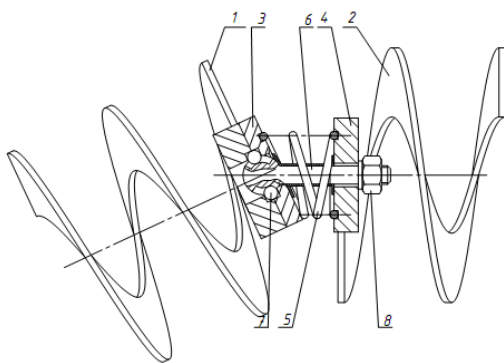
Конструктивна схема гвинтового секційного робочого органу конвеєра: 1, 2 – спіралі; 3 і 4 – оправки; 5 – пружина; 6 – шарнірне болтове з'єднання; 7 – кувалька; 8 – гайка
